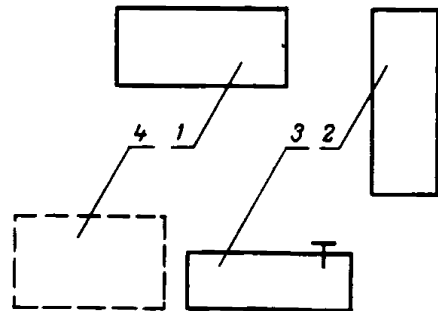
Типовая схема планировки рабочего места разборки и сборки механизма рулевого управления:
